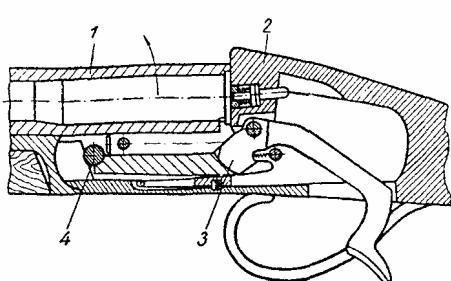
Схема ружья с неподвижным затвором и откидывающимся стволов:
